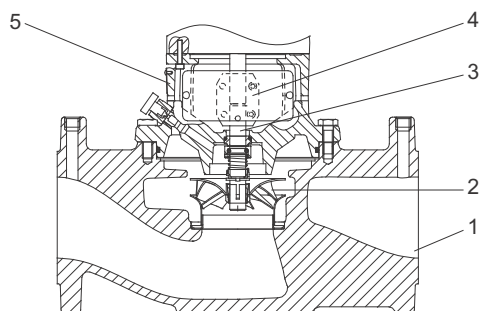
Rysunek przekrojowy pompy TP serii 100 z przyłączem gwintowanym
